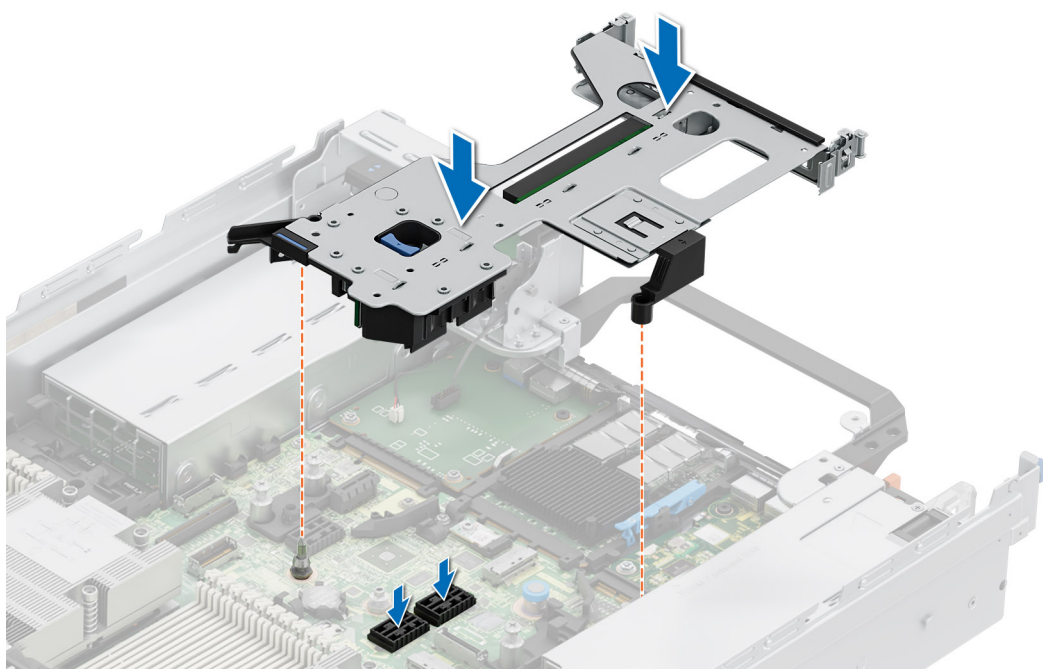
Installation de la carte de montage pour carte d'extension (carte de montage 2)
